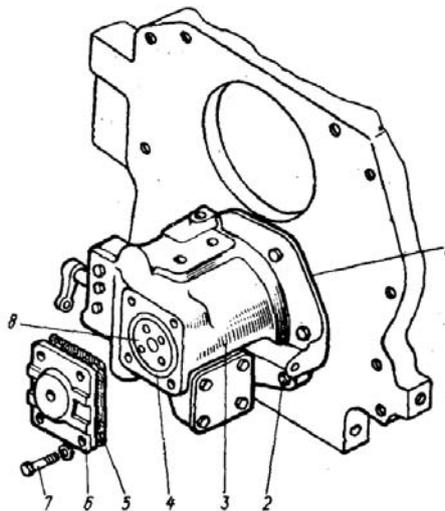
Установка гидрораспределителя: 1, 5 — прокладка; 2, 7 — болт; 3 — гидрораспределитель; 4 — кольцо; 6 — крышка; 8 — вал
